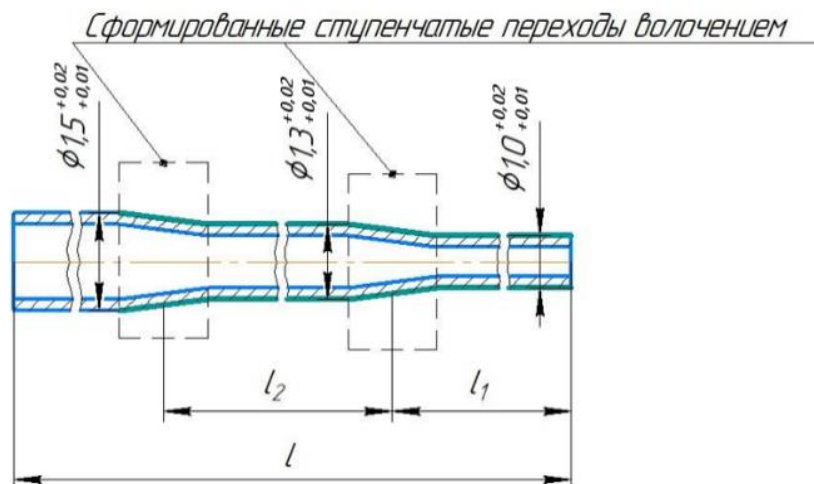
Чертеж-схема формирования ступенчатой заготовки
